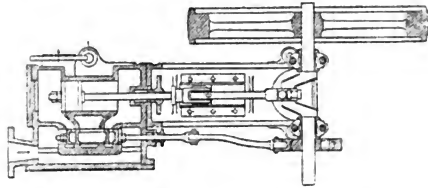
Mayers Wasserdruckmotor (Grundriss).
